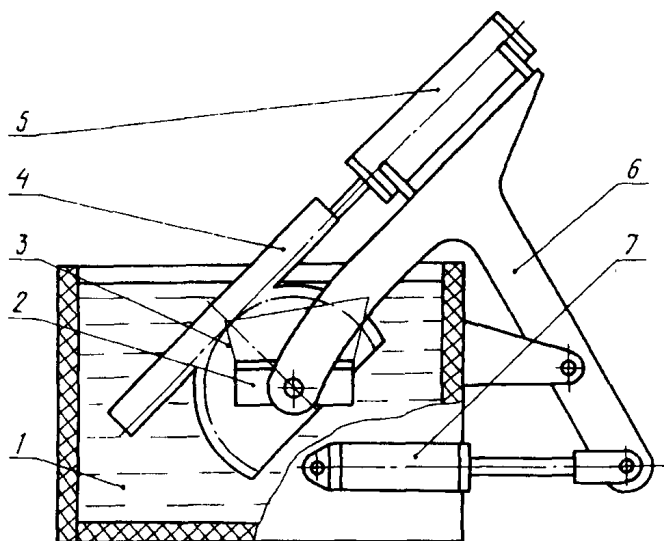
Стенд для контроля герметичности головки цилиндров
